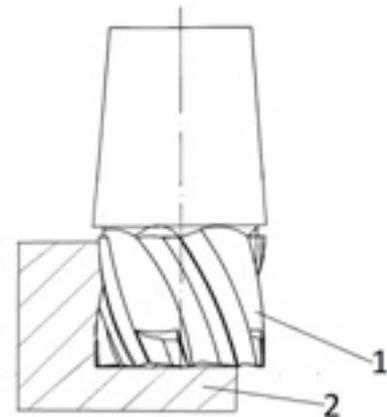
Взаимное положение концевой фрезы и детали с узким пазом.
